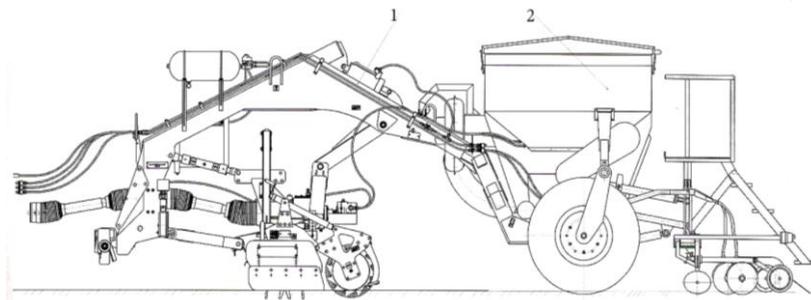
Общий вид агрегата почвообрабатывающе-посевного АППА-4 с активными рабочими органами: 1 – адаптер почвообрабатывающий; 2 – сеялка
